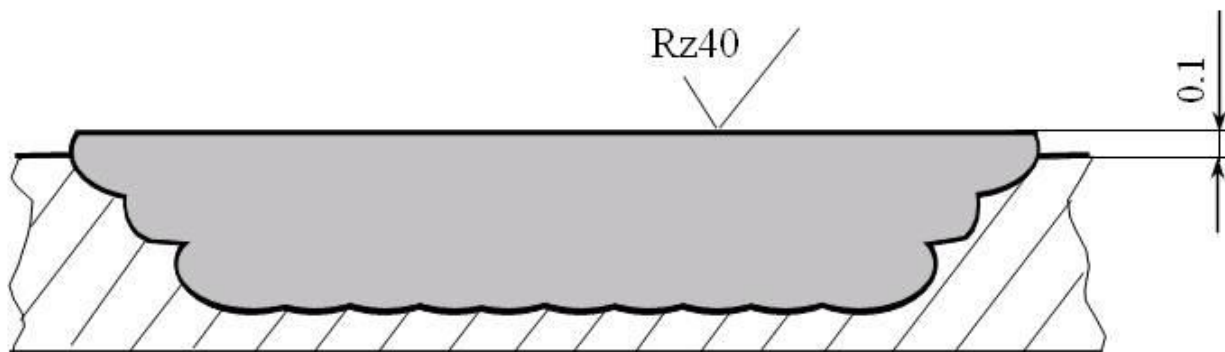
Параметры заварки выборки после механической обработки поверхности сварного шва
